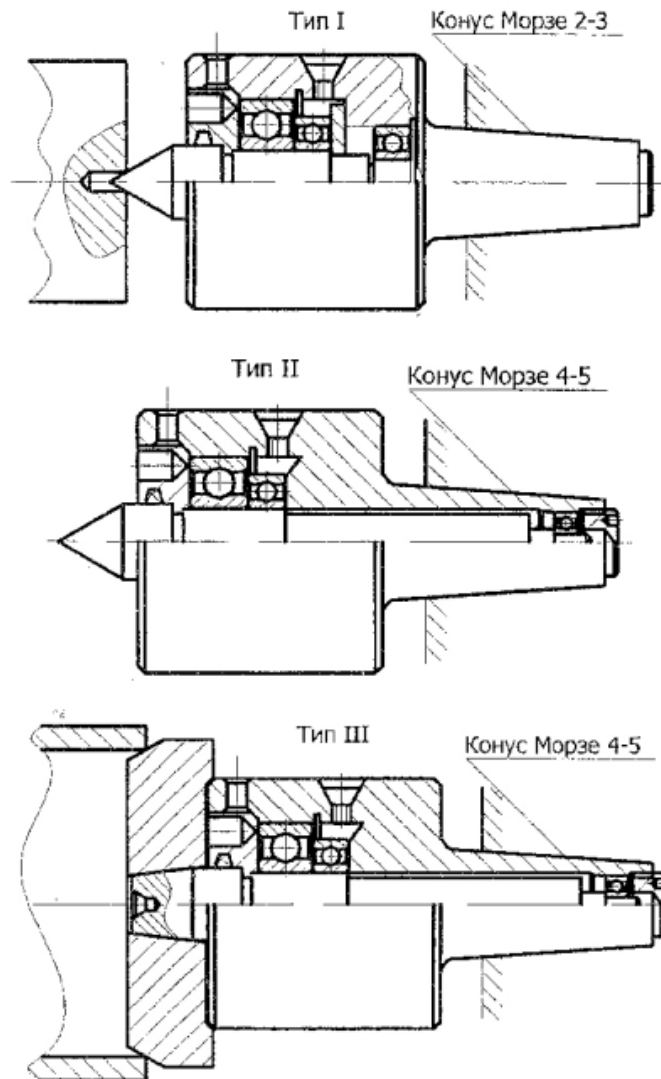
Конструкции вращающихся центров: тип I и II – для установки заготовок по центровым отверстиям; тип III – для установки полых деталей.
